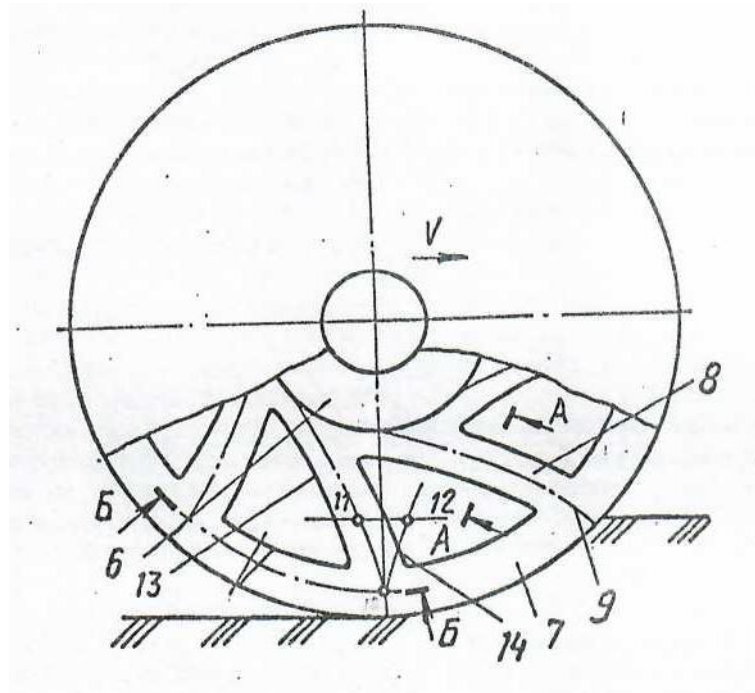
Визначення форми робочої поверхні спиці пасивного диска
